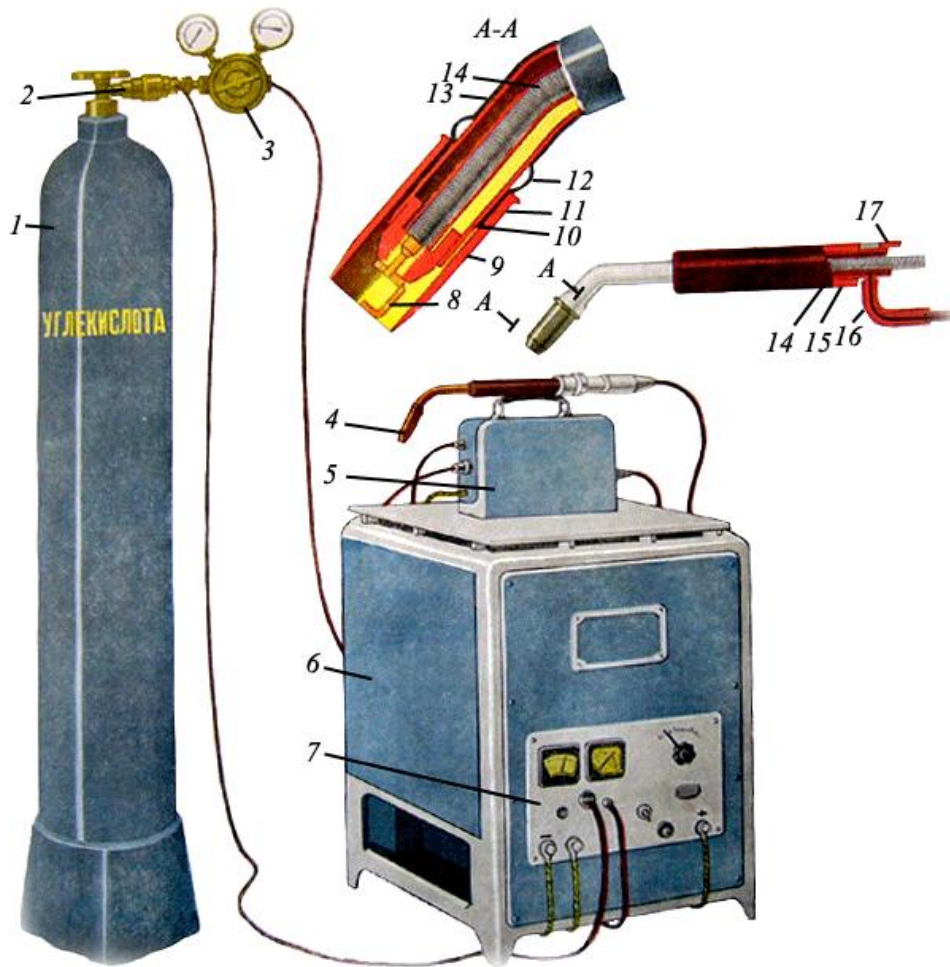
Напіваавтомат для зварювання в захисному газі:
